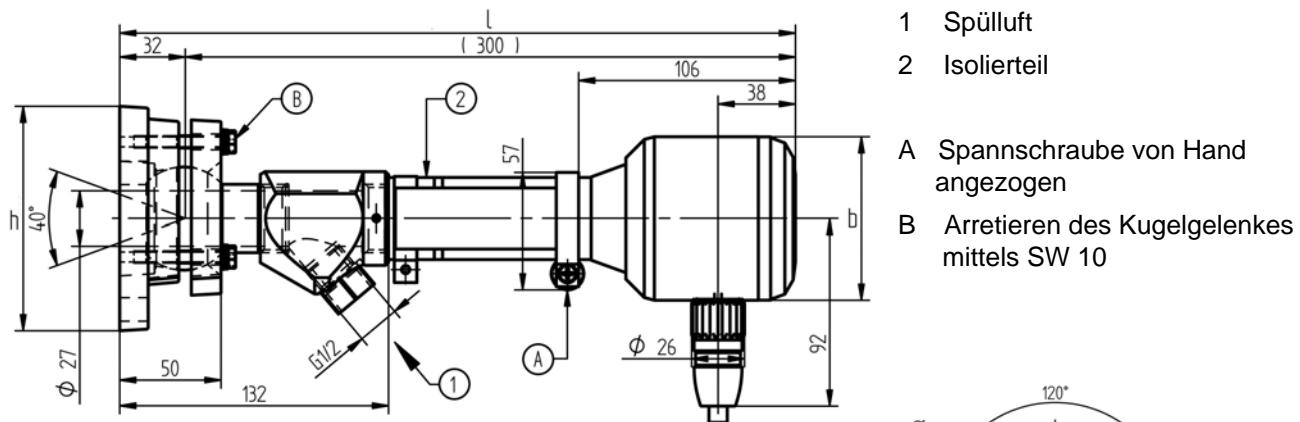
Maßbild FH40-10 Typ 659S1600 mit Flammenwächter F200K
